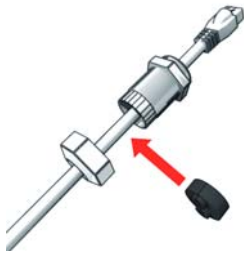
Kabelführung durch Kabelverschraubungen
